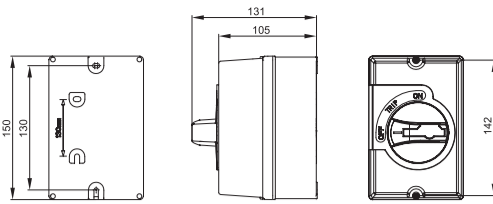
Габаритные и установочные размеры оболочки защитной / Figure 3 – Overall and mounting dimensions of the protective enclosure / 3 сурет – Қорғаныш қабықшасының габариттік және орнату өлшемдері
